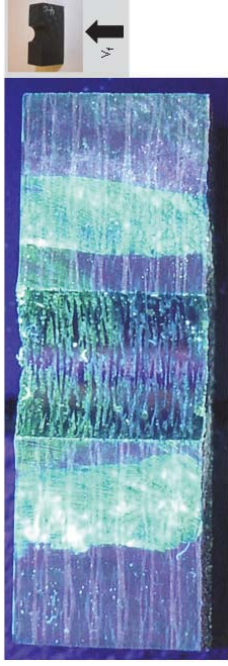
Eindringprüfung für Werkzeug D11 Bohrung 803
